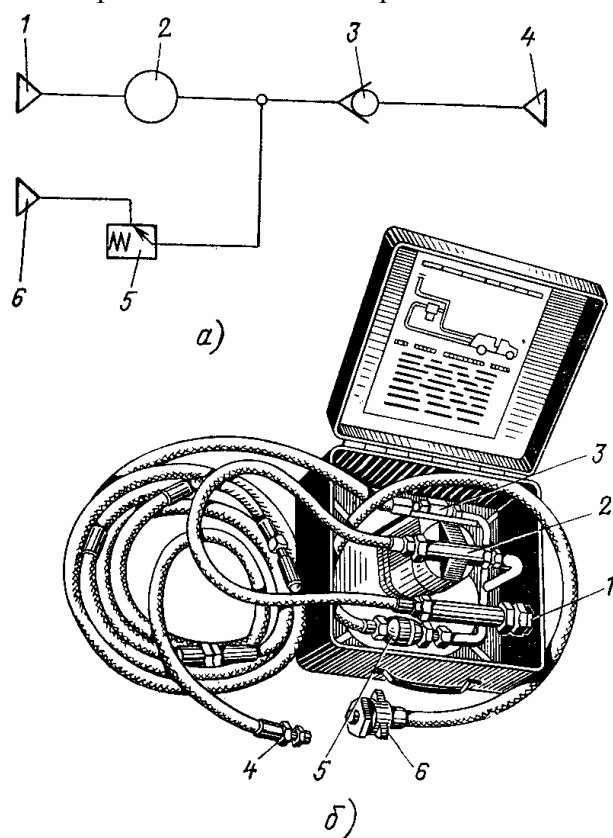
Приспособление 154.00.9960.300 для консервации топливной системы двигателя:
